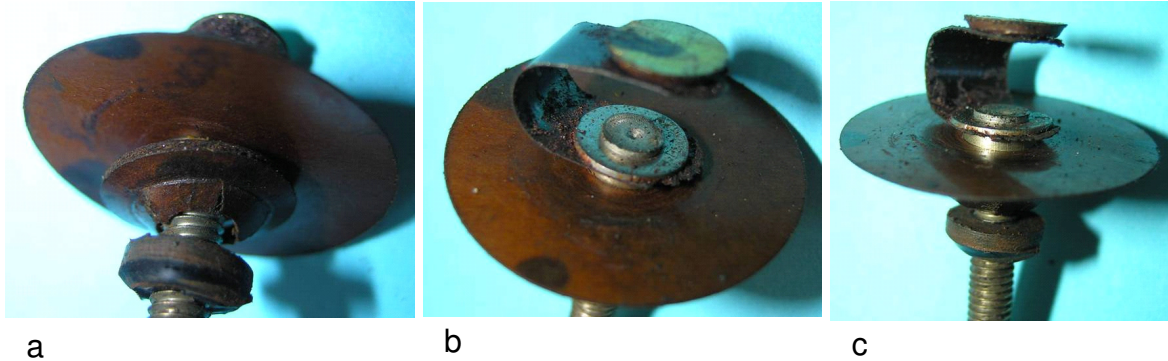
Kabelbolzen mit Blattfeder und Kontaktelement
